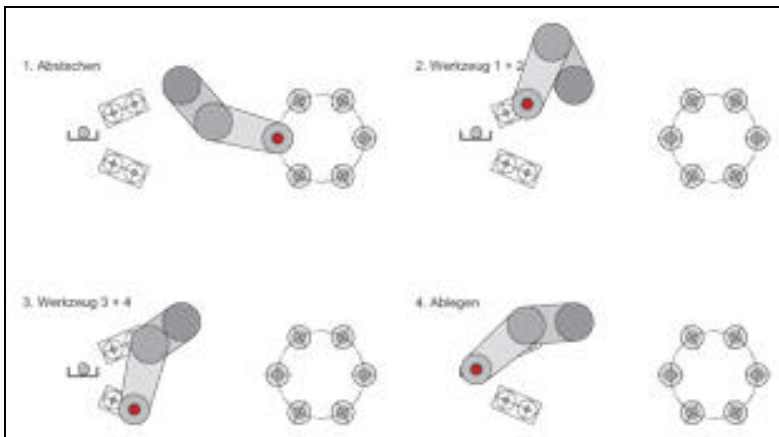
Rückseitenbearbeitung mit 4 Werkzeugen
